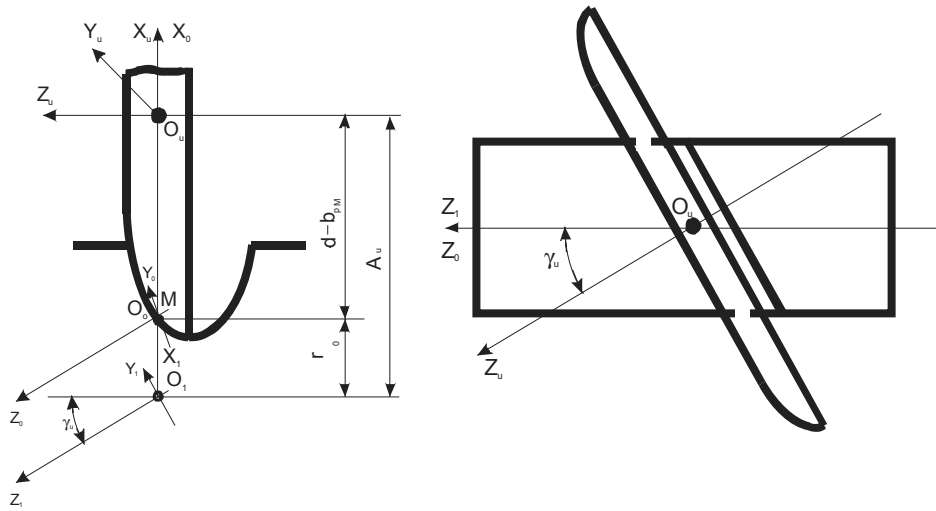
Розташування шліфувального круга при обробці поверхні черв'яка
